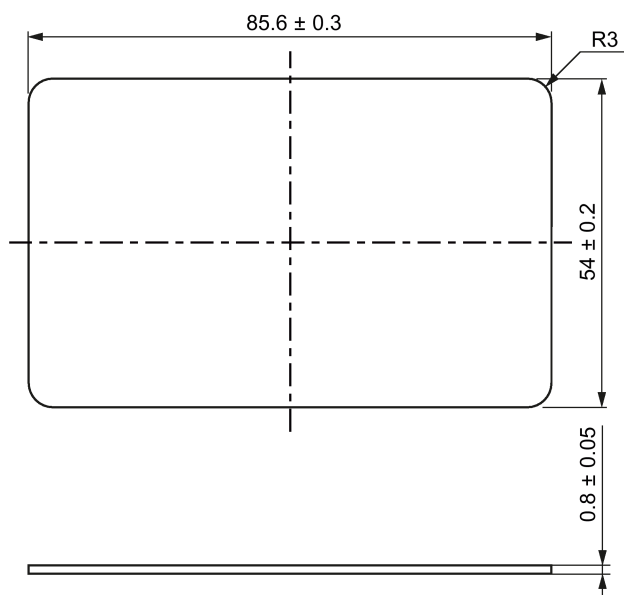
Desenho de dimensões MDS D400 (medidas em mm)
